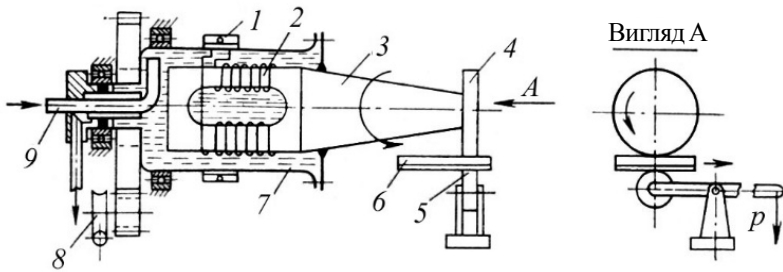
Схема установки для шовного зварювання ультразвуком:
